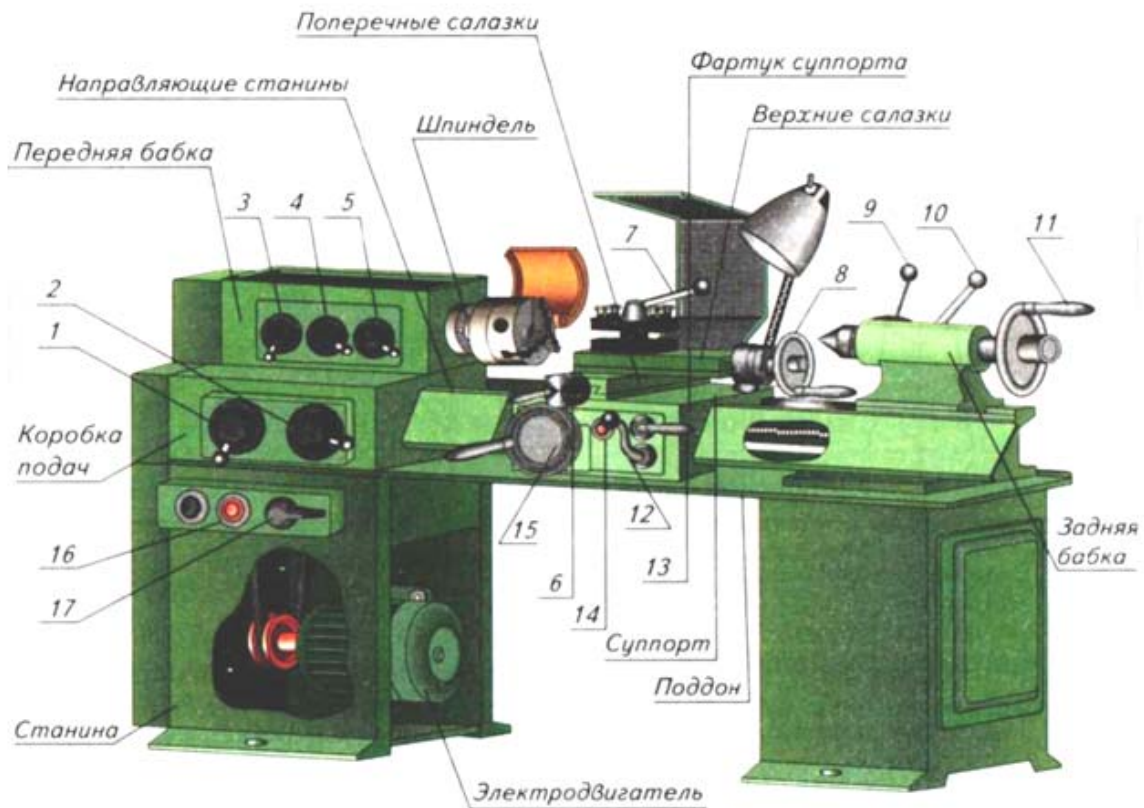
Токарно-винторезный станок ТВ-6: 1,2 – рукоятки переключения величины подачи; 3 – рукоятка переключения гитарного механизма; 4, 5 – рукоятки переключения частоты вращения шпинделя; 6 – рукоятка поперечной подачи суппорта; 7 – рукоятка закрепления резцедержателя; 8 – рукоятка перемещения верхних салазок; 9 – рукоятка крепления пиноли; 10 – рукоятка крепления задней бабки; 11 – маховик подачи пиноли; 12, 13 – рукоятки управления механической подачей; 14 – кнопка включения реечной передачи; 15 – маховик перемещения суппорта; 16 – кнопки включения и отключения электродвигателя; 17 – рукоятка реверса
